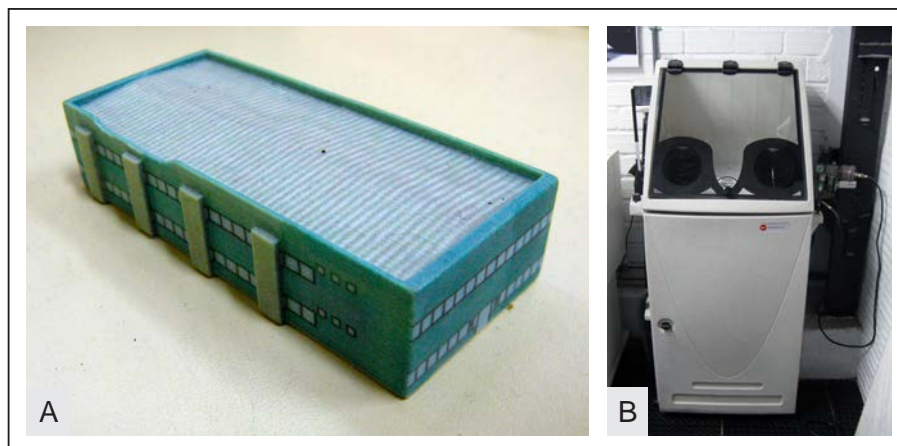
ZCorp 510: detalhe da câmara de construção.
